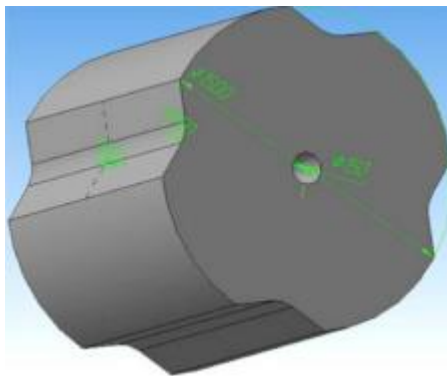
3D-модель профилированной заготовки на четырехлучевое сечение
